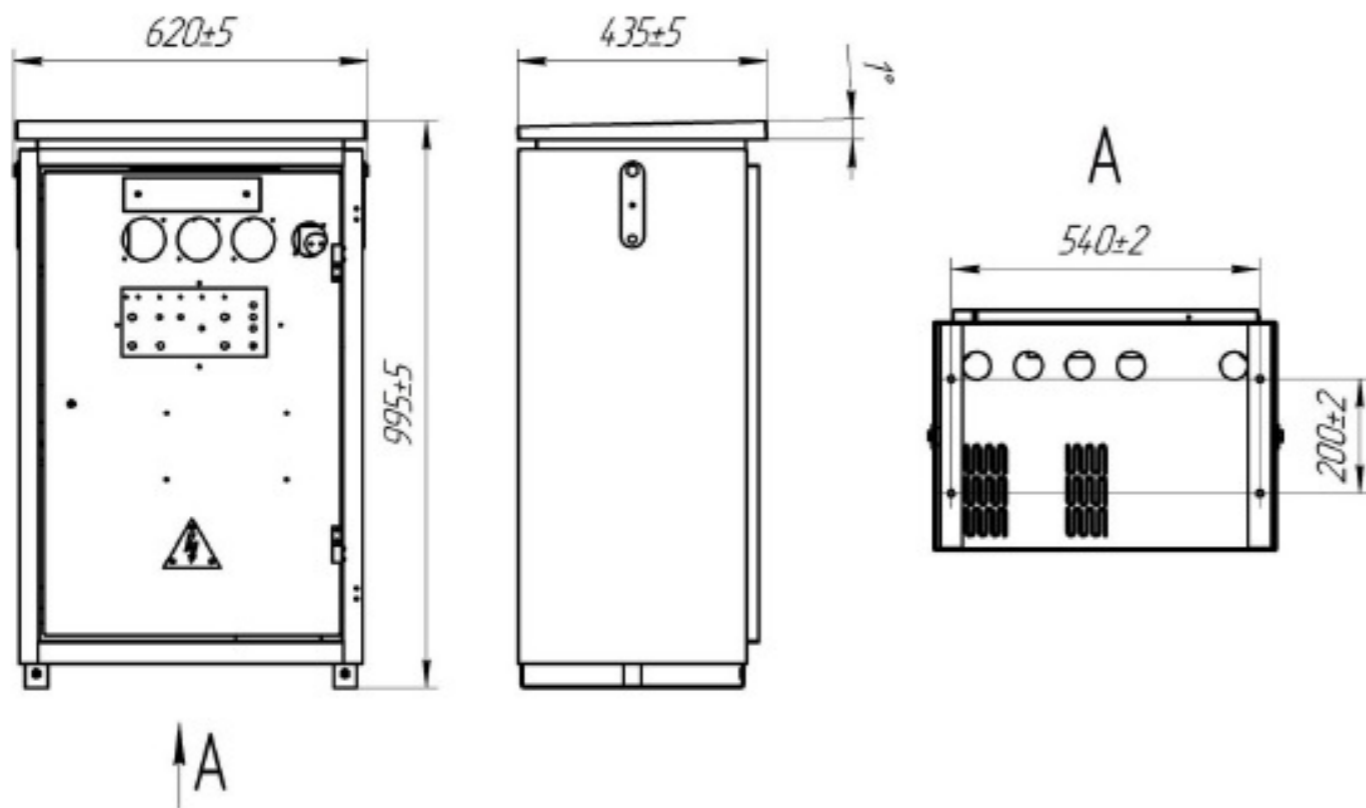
Габаритные и установочные размеры В-ОПЕ для типоразмера У2
